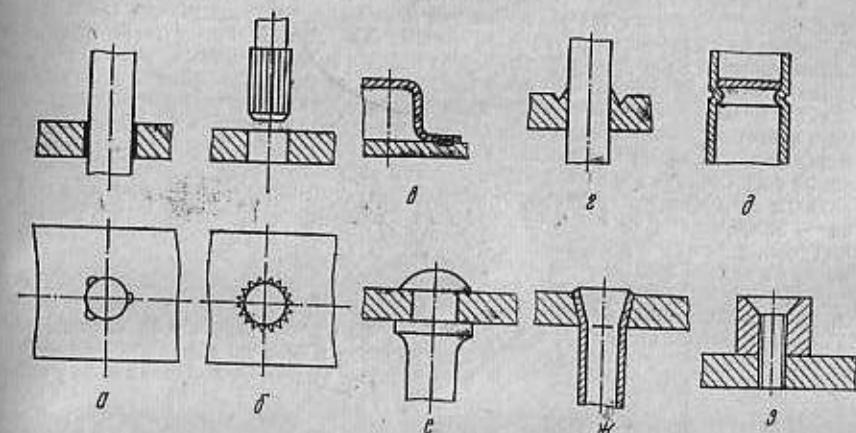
Способы закрепления элементов изделия при сборке и пайке:
